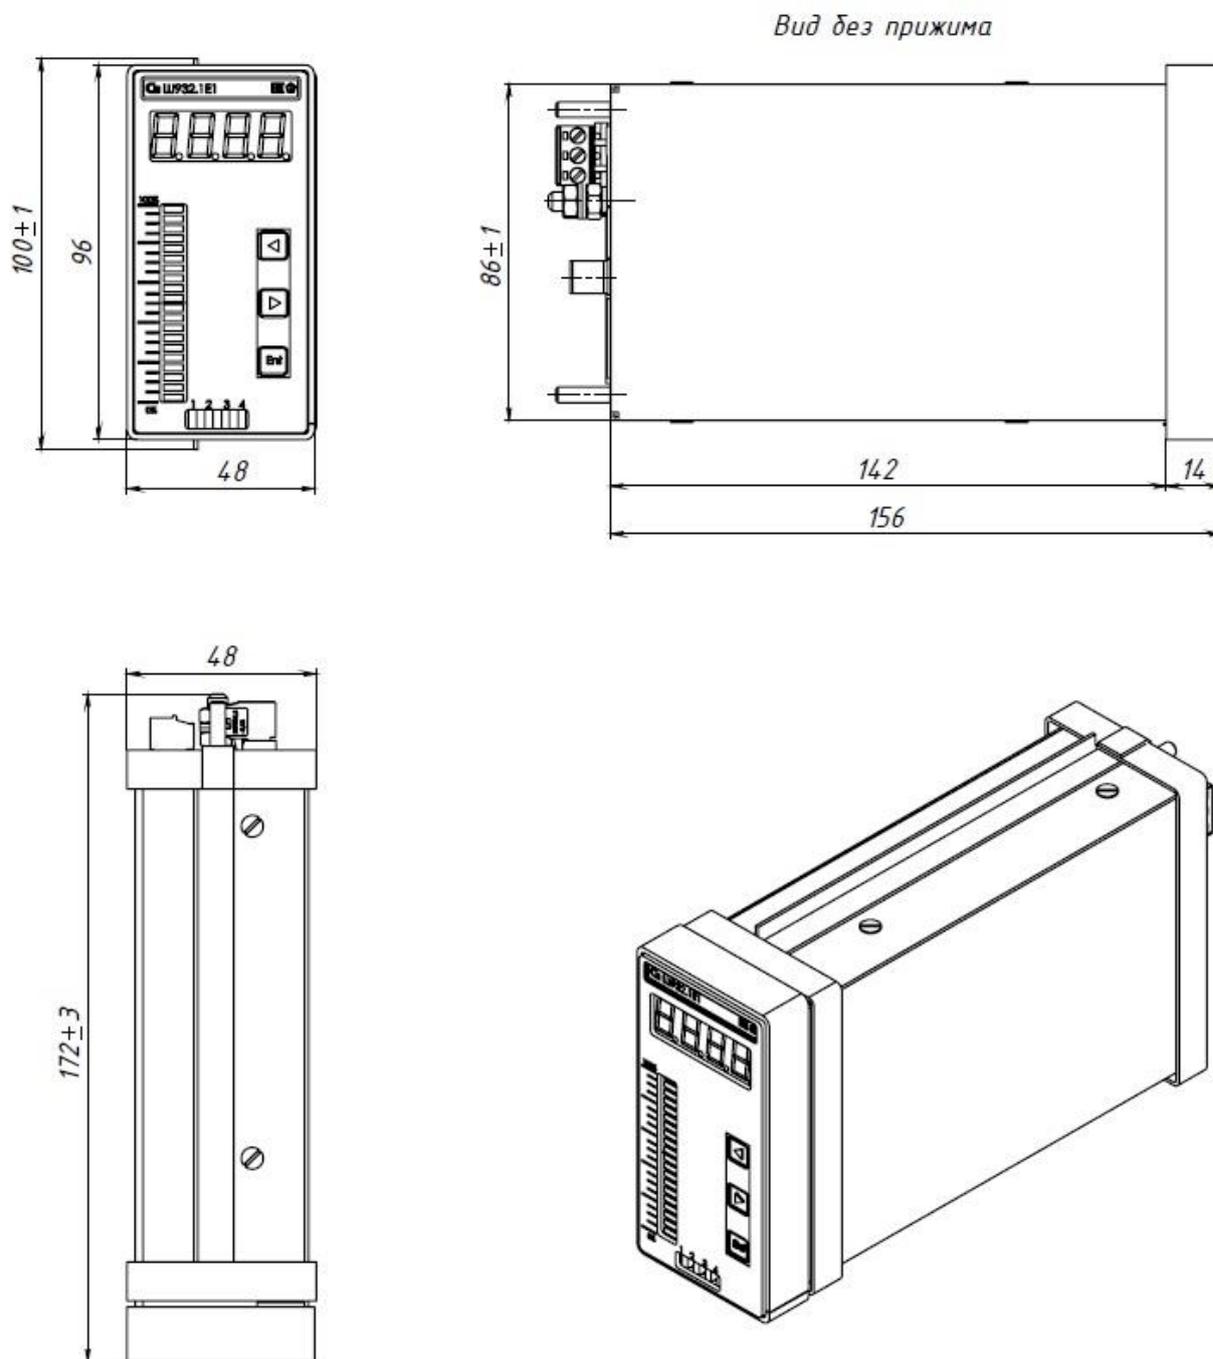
Габаритные и установочные размеры прибора Ш932.1Е1
